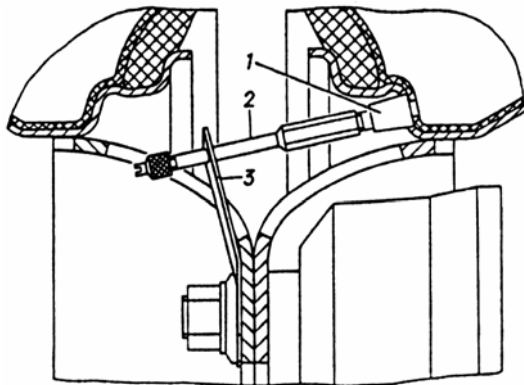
Установка удлинителя вентиля шин задних колес: 1 – вентиль; 2 – удлинитель; 3 – кронштейн
